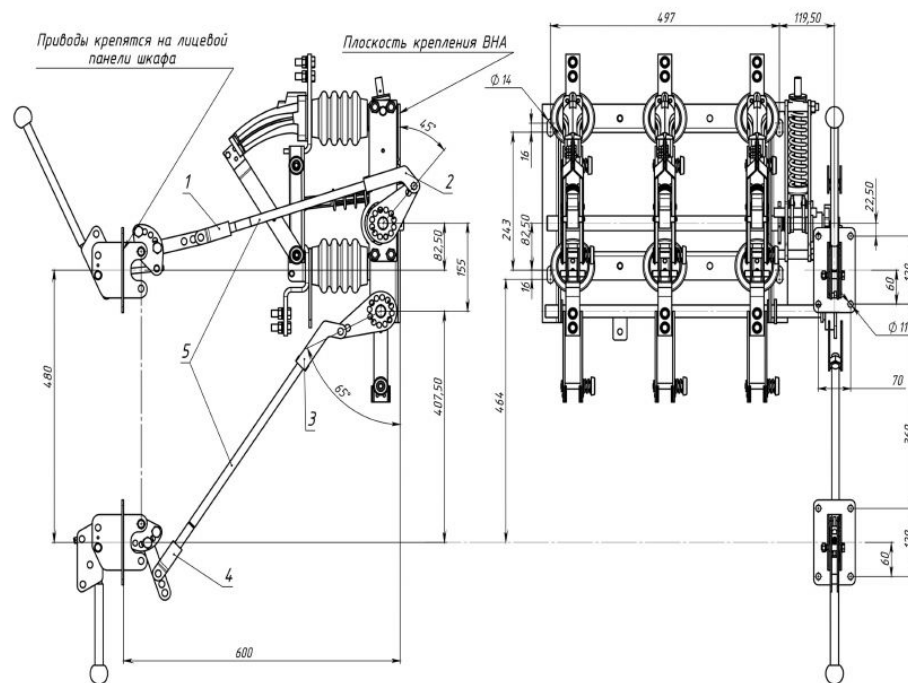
Возможный монтаж выключателя нагрузки с приводом ПРБД-10.
